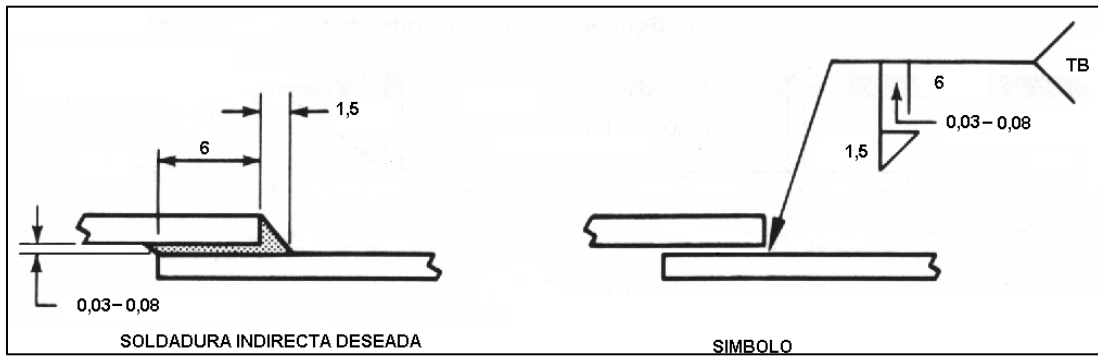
Aplicación de símbolos de soldadura indirecta en juntas traslapadas.
